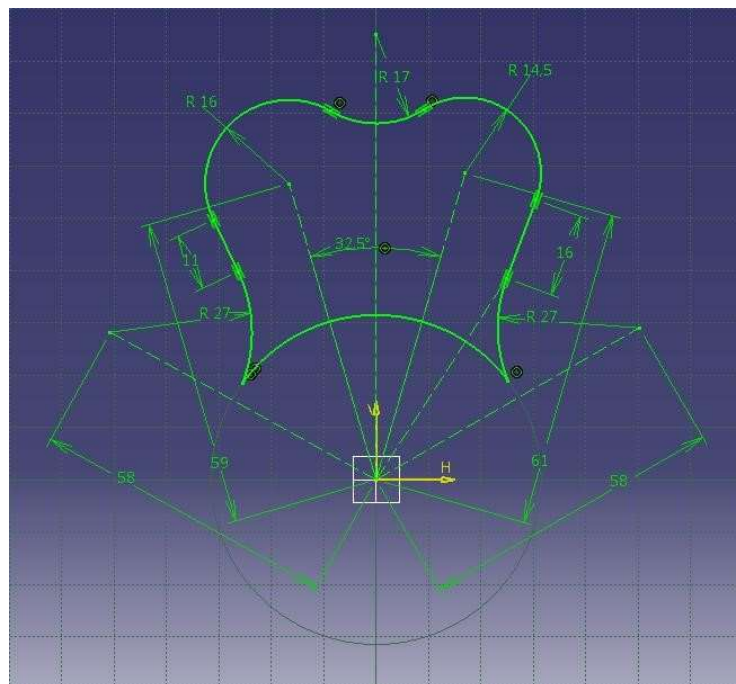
Dimensões da câmara entre as válvulas, adjacente ao cilindro.
